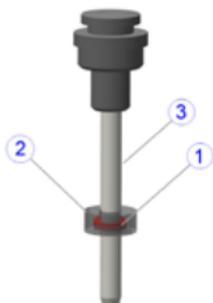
Aufsetzen der Ringe auf die Kolbenstange
